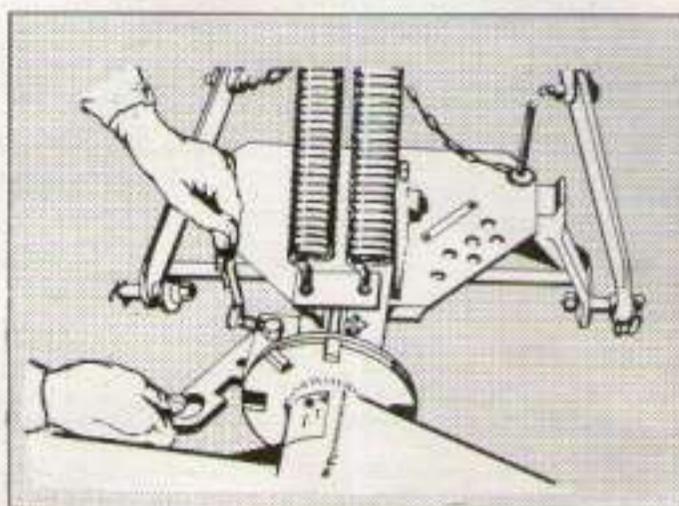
VERROUILLAGE DE LA POUTRE EN POSITION HORIZONTALE
